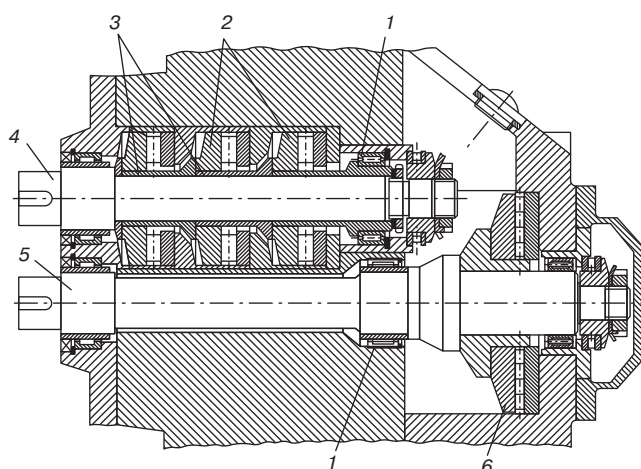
Схема узла подшипников двухшнекового экструдера с одним упорным подшипником большого диаметра и тремя подшипниками малого диаметра: 1 — игольчатый радиальный подшипник; 2 — упорные однорядные подшипники; 3 — дистанционные втулки; 4, 5 — приводные валы; 6 — упорный многорядный подшипник
